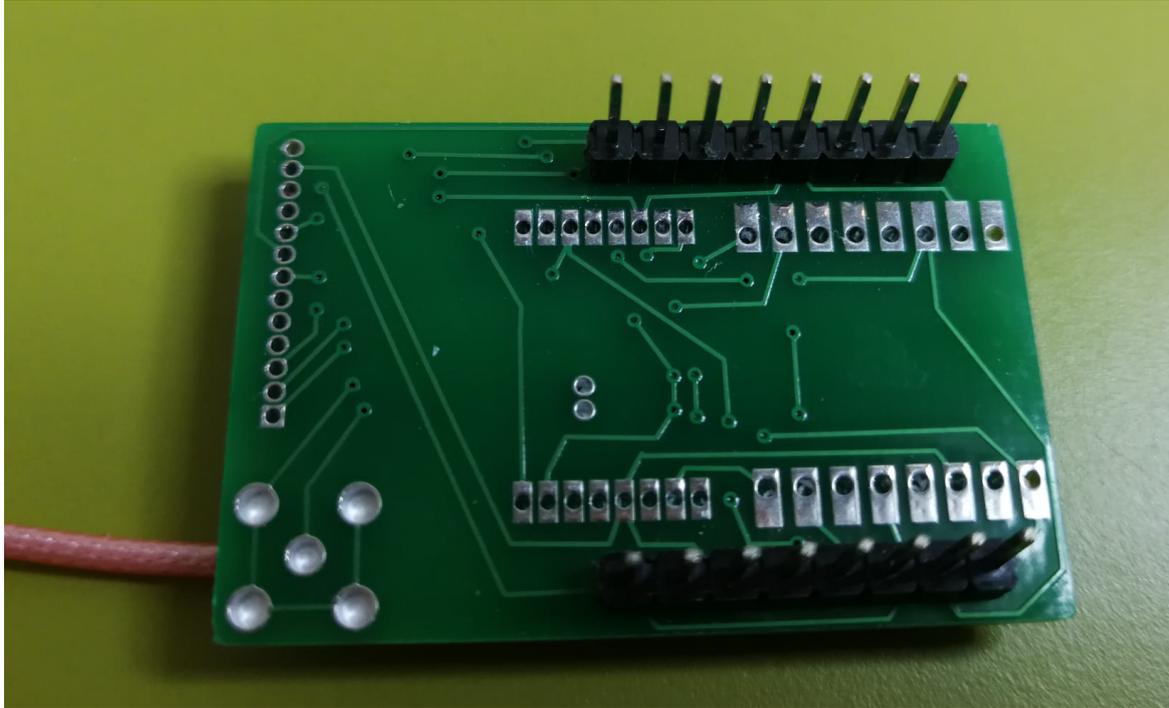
LoRa carrier : LoRa module montato su relativo PCB carrier lato inferiore
